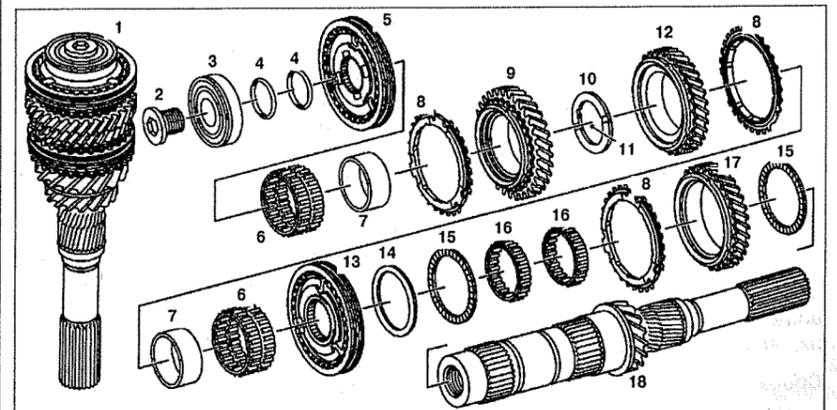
Ведущий вал (автомобили с двигателями 111.948 и 601.970):
